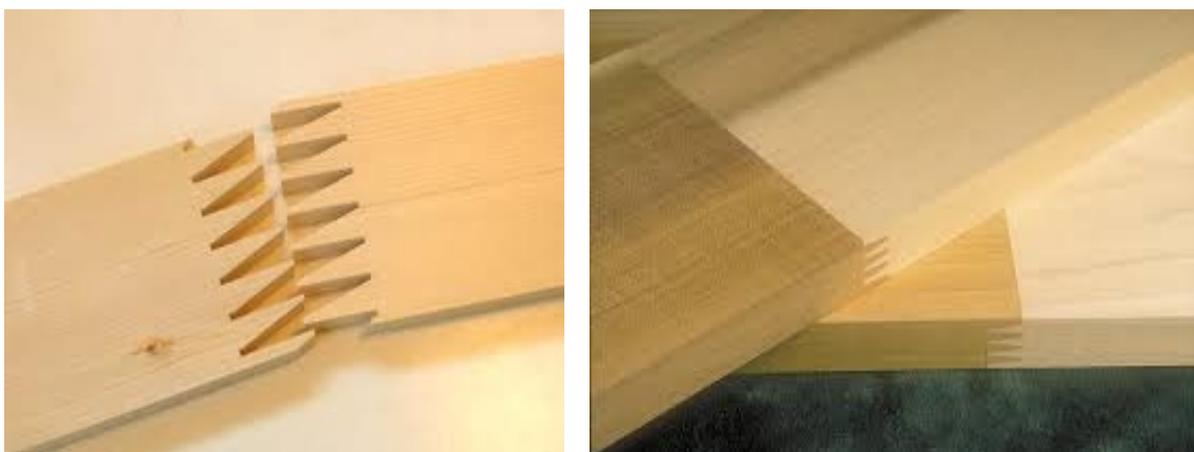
União com “finger joints” horizontal e vertical para fabricação de “blanks” a partir de "clear-blocks".
